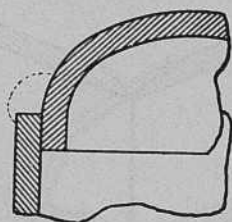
Soldadura defectuosa de un fondo de recipiente.
